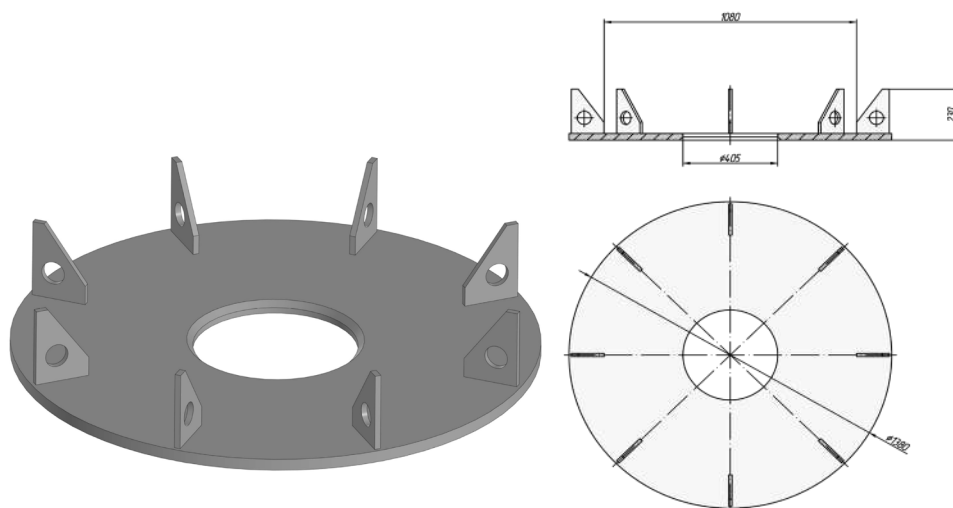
Кондуктор для центровки перегрузочного контейнера
